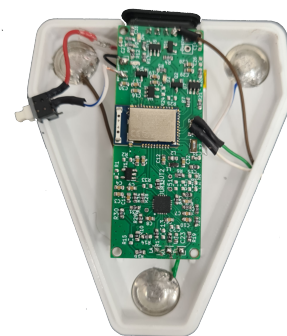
Montaje final del dispositivo ECG portátil. Fuente: Elaboración propia.
